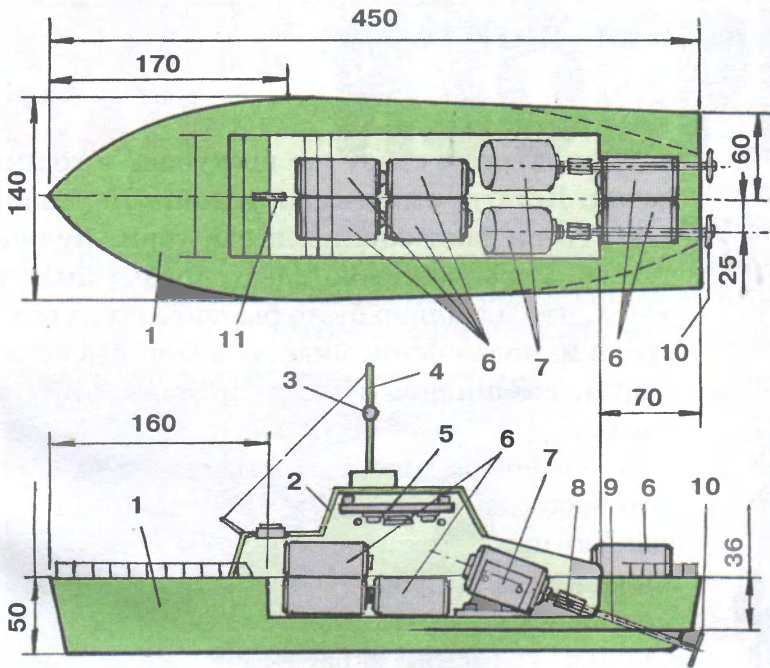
Компоновка узлов и деталей модели: 1 — корпус; 2 — рубка; 3 — фотодиод; 4 — мачта; 5 — плата управления; 6 — батареи питания; 7 — электродвигатель; 8 — муфта; 9 — вал; 10 — винт; 11 — выключатель.
